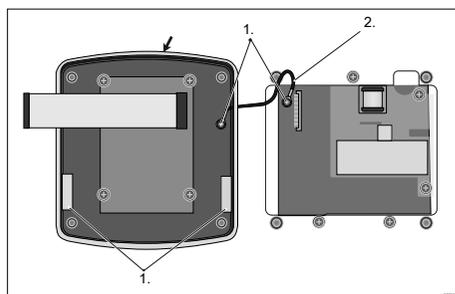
En cas de montage encastré : Monter le joint profilé sur la partie supérieure du boîtier du régulateur
